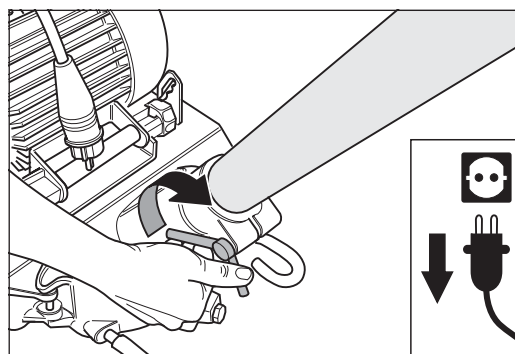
Nach dem Einbau des Führungsrohrs die Flügelmutter am Maschinengehäuse sorgfältig festziehen.
